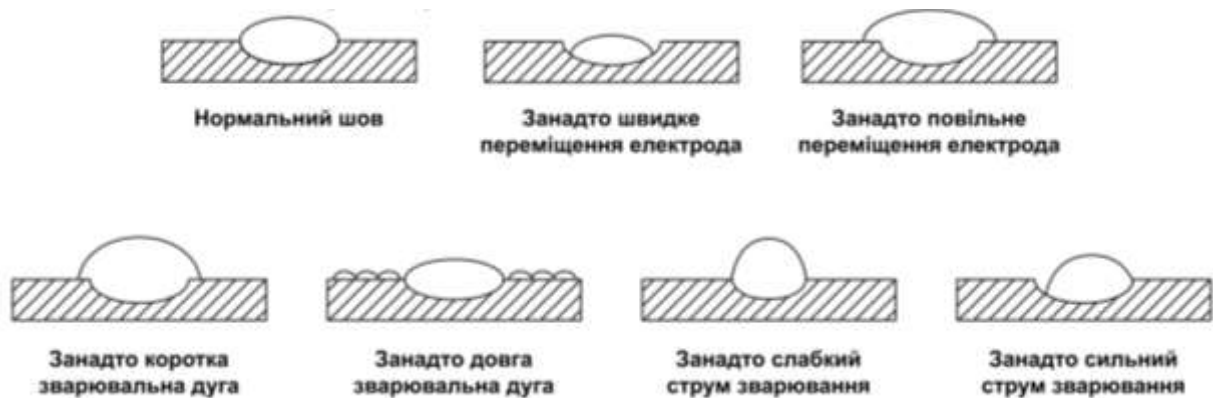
Основні види помилок, які можуть виникати під час MIG/MAG зварювання
